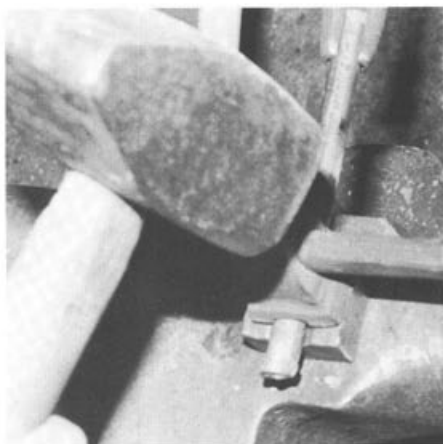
Auch beim Gesenkschmieden müssen Schmied und Zuschläger zusammenwirken. Im Amboss steckt das Gesenk, und der Schmied führt den in Form und Grösse passenden Gesenkhammer. Dazwischen wird das Werkstück geformt, hier ein runder Stab, der auf einen geringeren Querschnitt reduziert wird.
